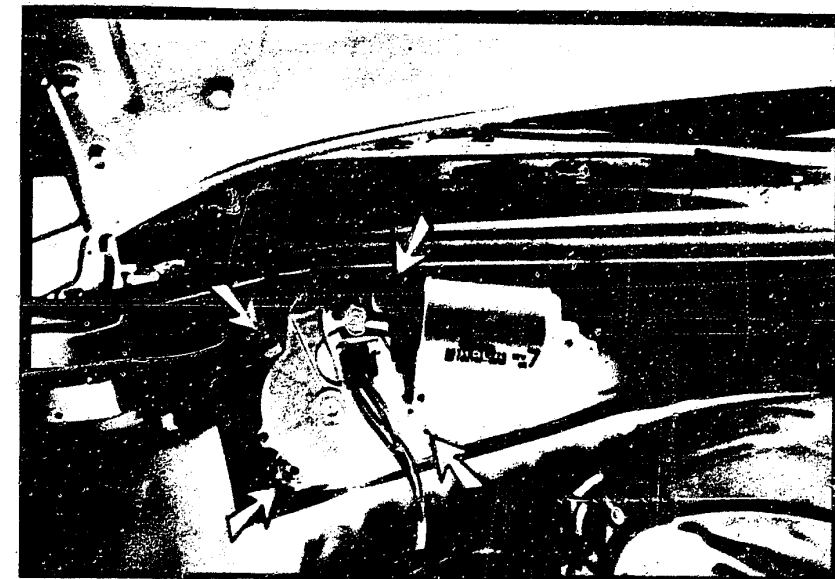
Für den Ausbau des Wischermotors sind die vier Schrauben (Pfeile zu lösen.
